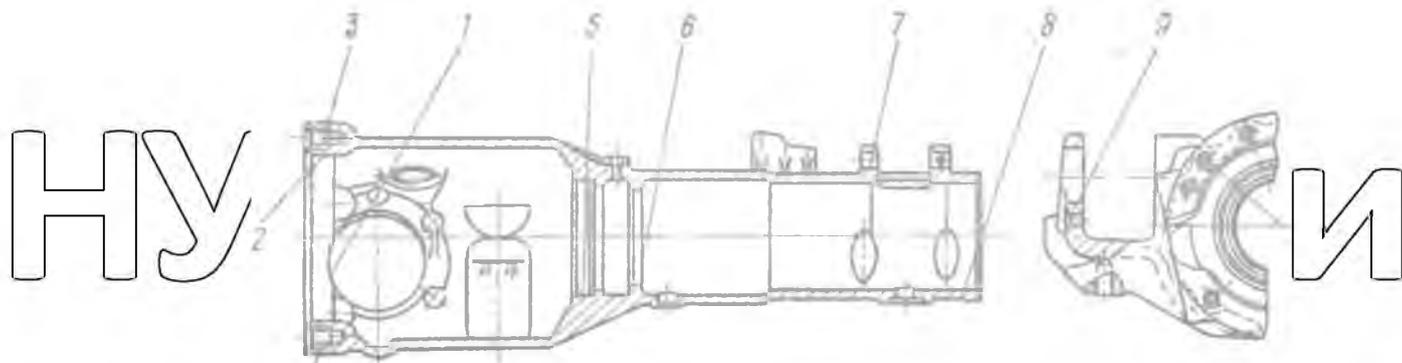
Корпус 52-2301055-А3. Матеріал — відливка 40Л; маса 36,2 кг; твердість — 143...217 НВ
